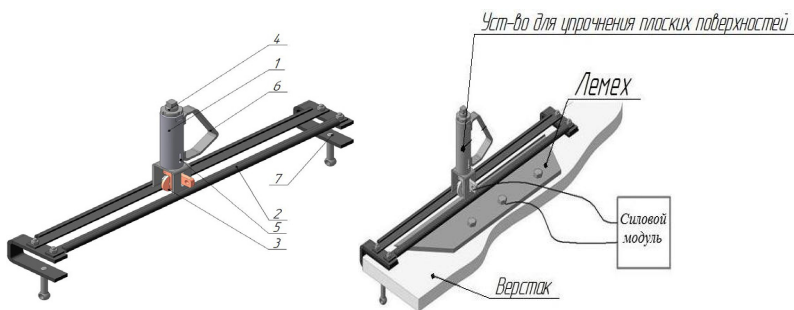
Приспособление для электромеханической закалки плоских поверхностей: 1 - телескопическая державка; 2 - направляющие; 3 - бронзовый ролик, 4 - винт поджатия; 5 - выносной флажок; 6 - ручка для перемещения; 7 - зажимные винты
